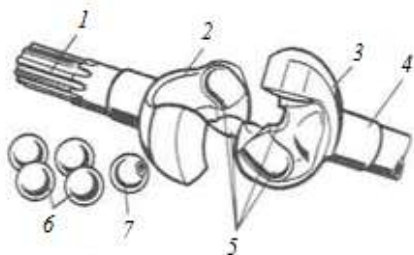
Кульковий карданний шарнір з ділильними канавками (типу «Вейс»): 1, 4 – приводні вали; 2, 3 – кулачки; 5 – канавки; 6, 7 – кульки
